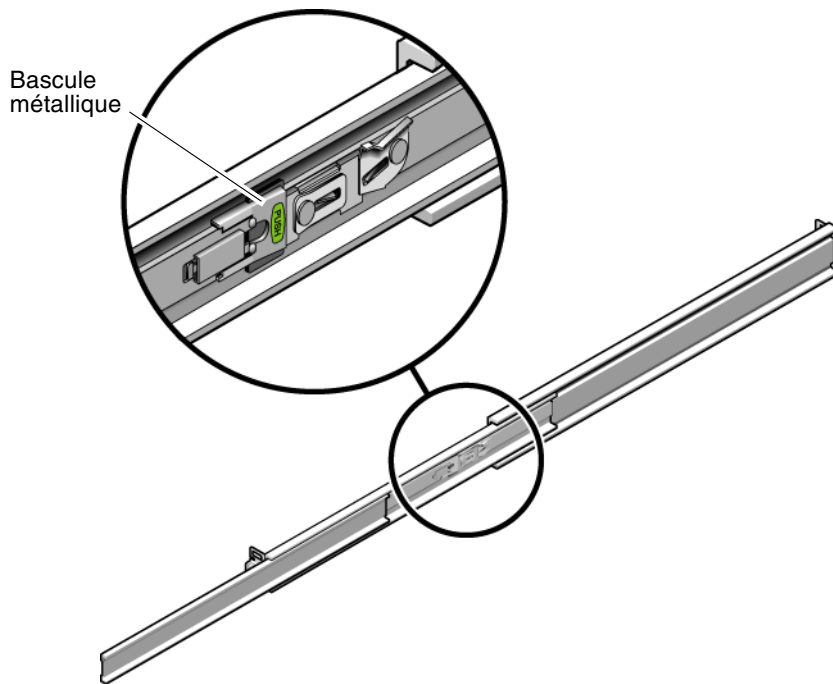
Déverrouillage de la section centrale d'un rail coulissant
